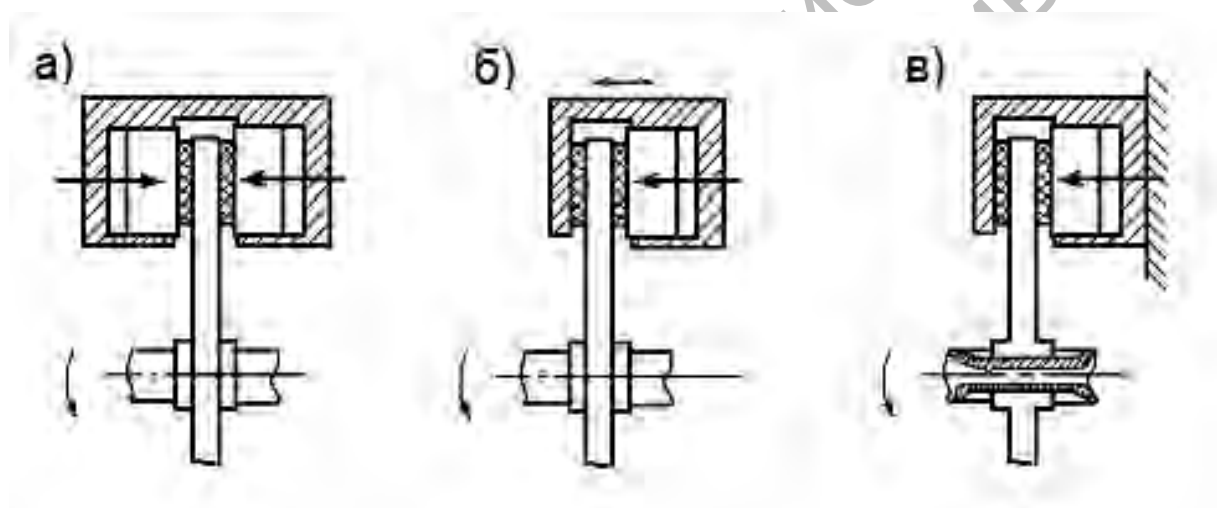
Схемы дисковых тормозов: а – с неподвижной скобой; б – с плавающей скобой; в – с неподвижной скобой и подвижным диском
